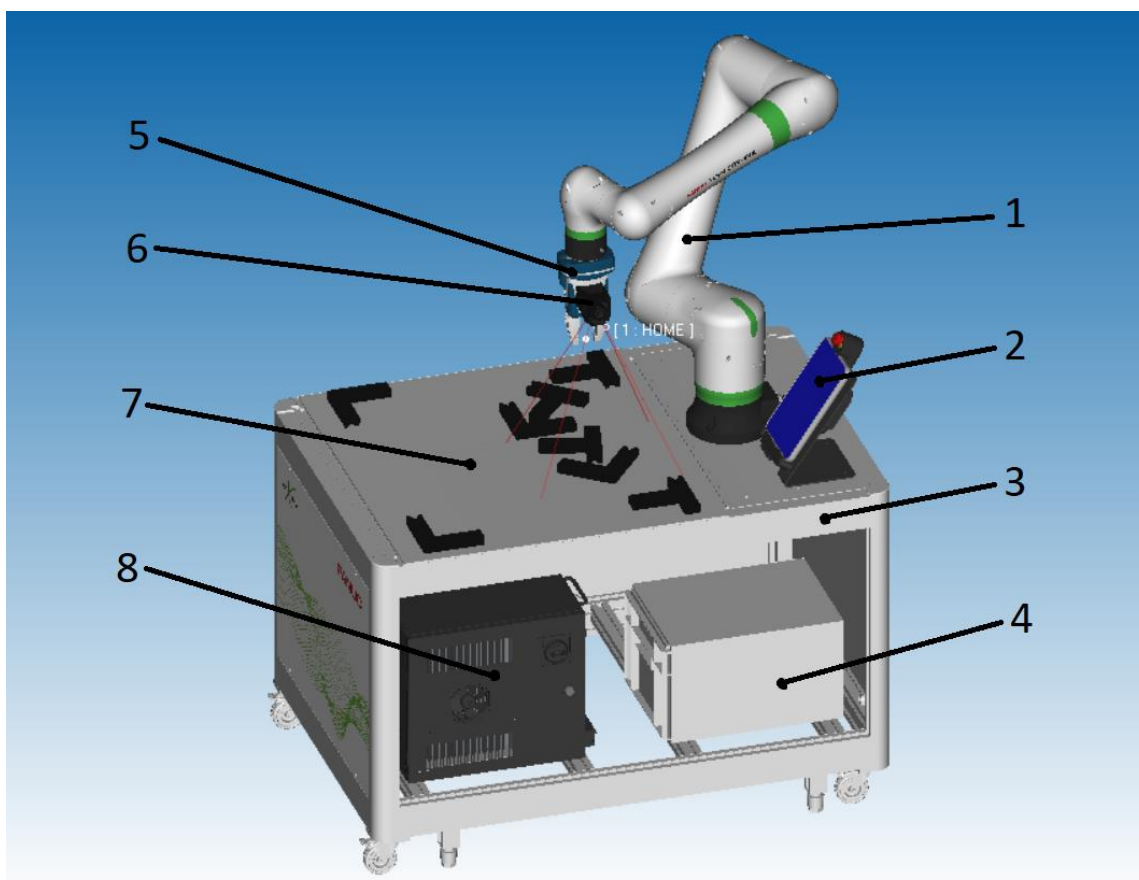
Layout pracovní plochy robotické buňky ER-4iA
